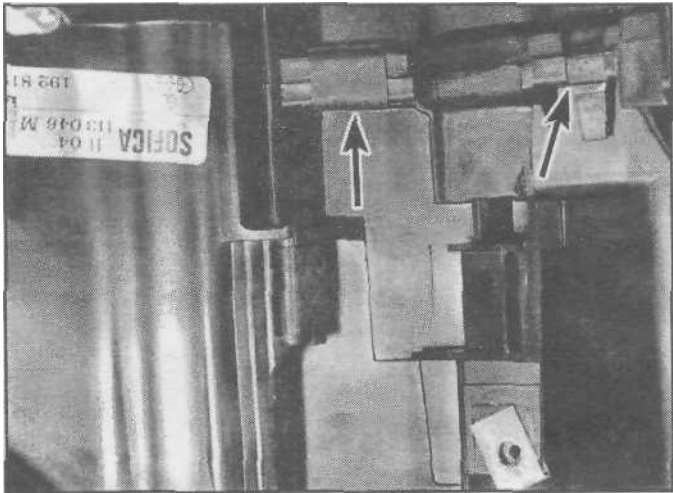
Защелки соединения верхнего и нижнего корпусов [показаны стрелками]
